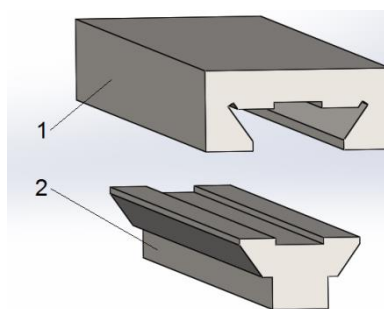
Разъемное соединение типа ласточкин хвост: 1 – охватывающая деталь; 2 – охватываемая деталь
